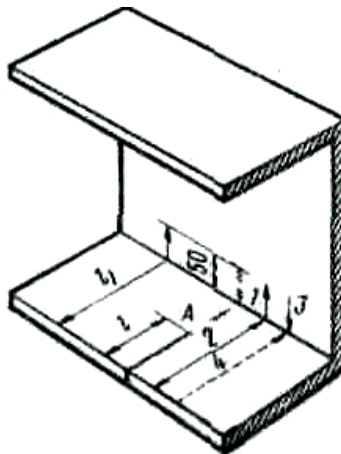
Ескіз підготовки і зварювання тріщини повздовжньої балки рами
